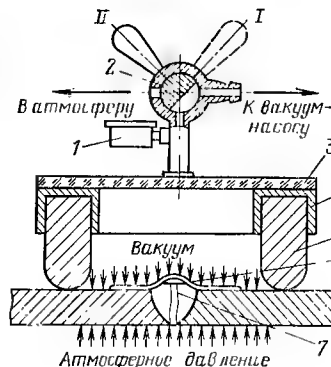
Схема вакуумного контроля сварных соединений с помощью плоской вакуум-камеры.
